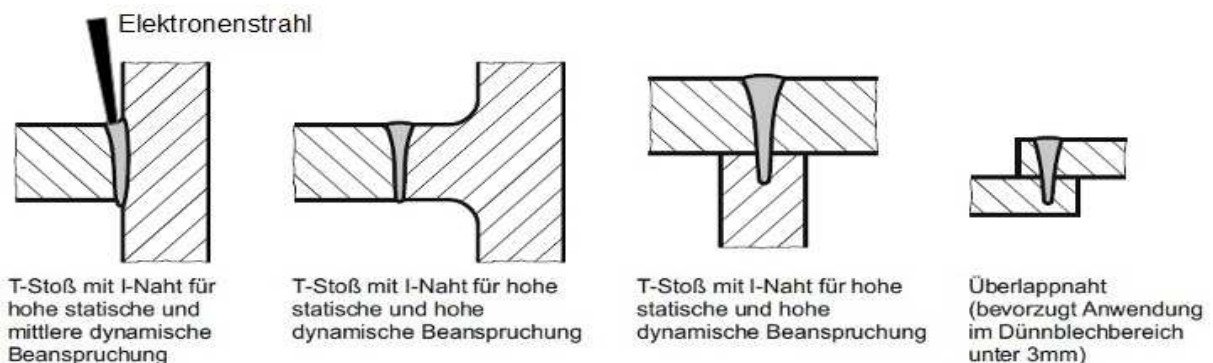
Sonstige Schweißnahtformen [4]
